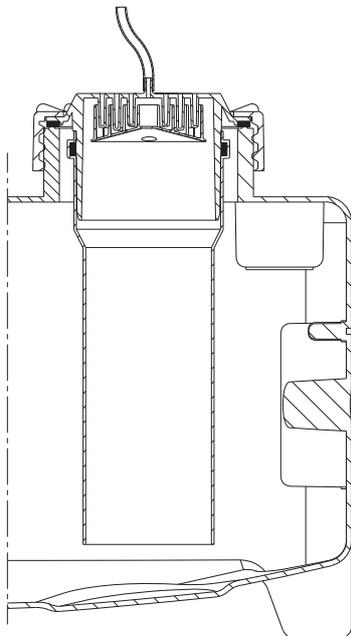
Крышка с резьбой и шланг, трубка DN 100 и уловитель конденсата
